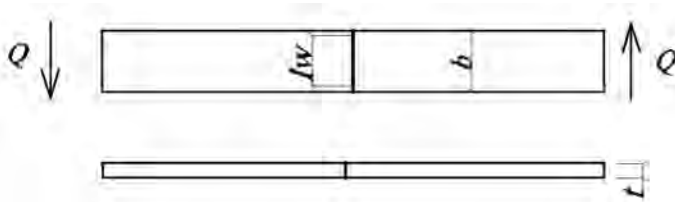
К расчету стыкового сварного шва на срез
